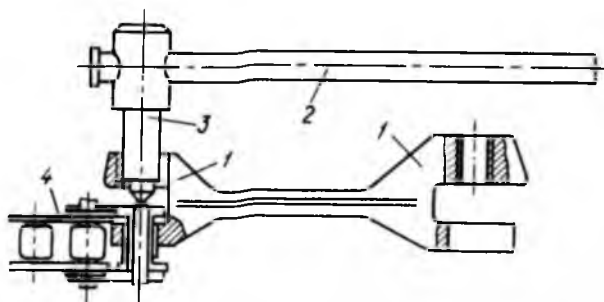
Приспособление для разъединения втулочно-роликовых цепей:
